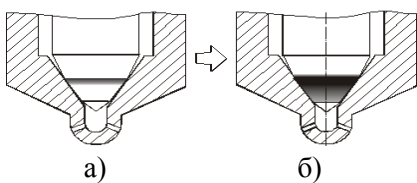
Схеми контакту голки і корпуса розпилювача
